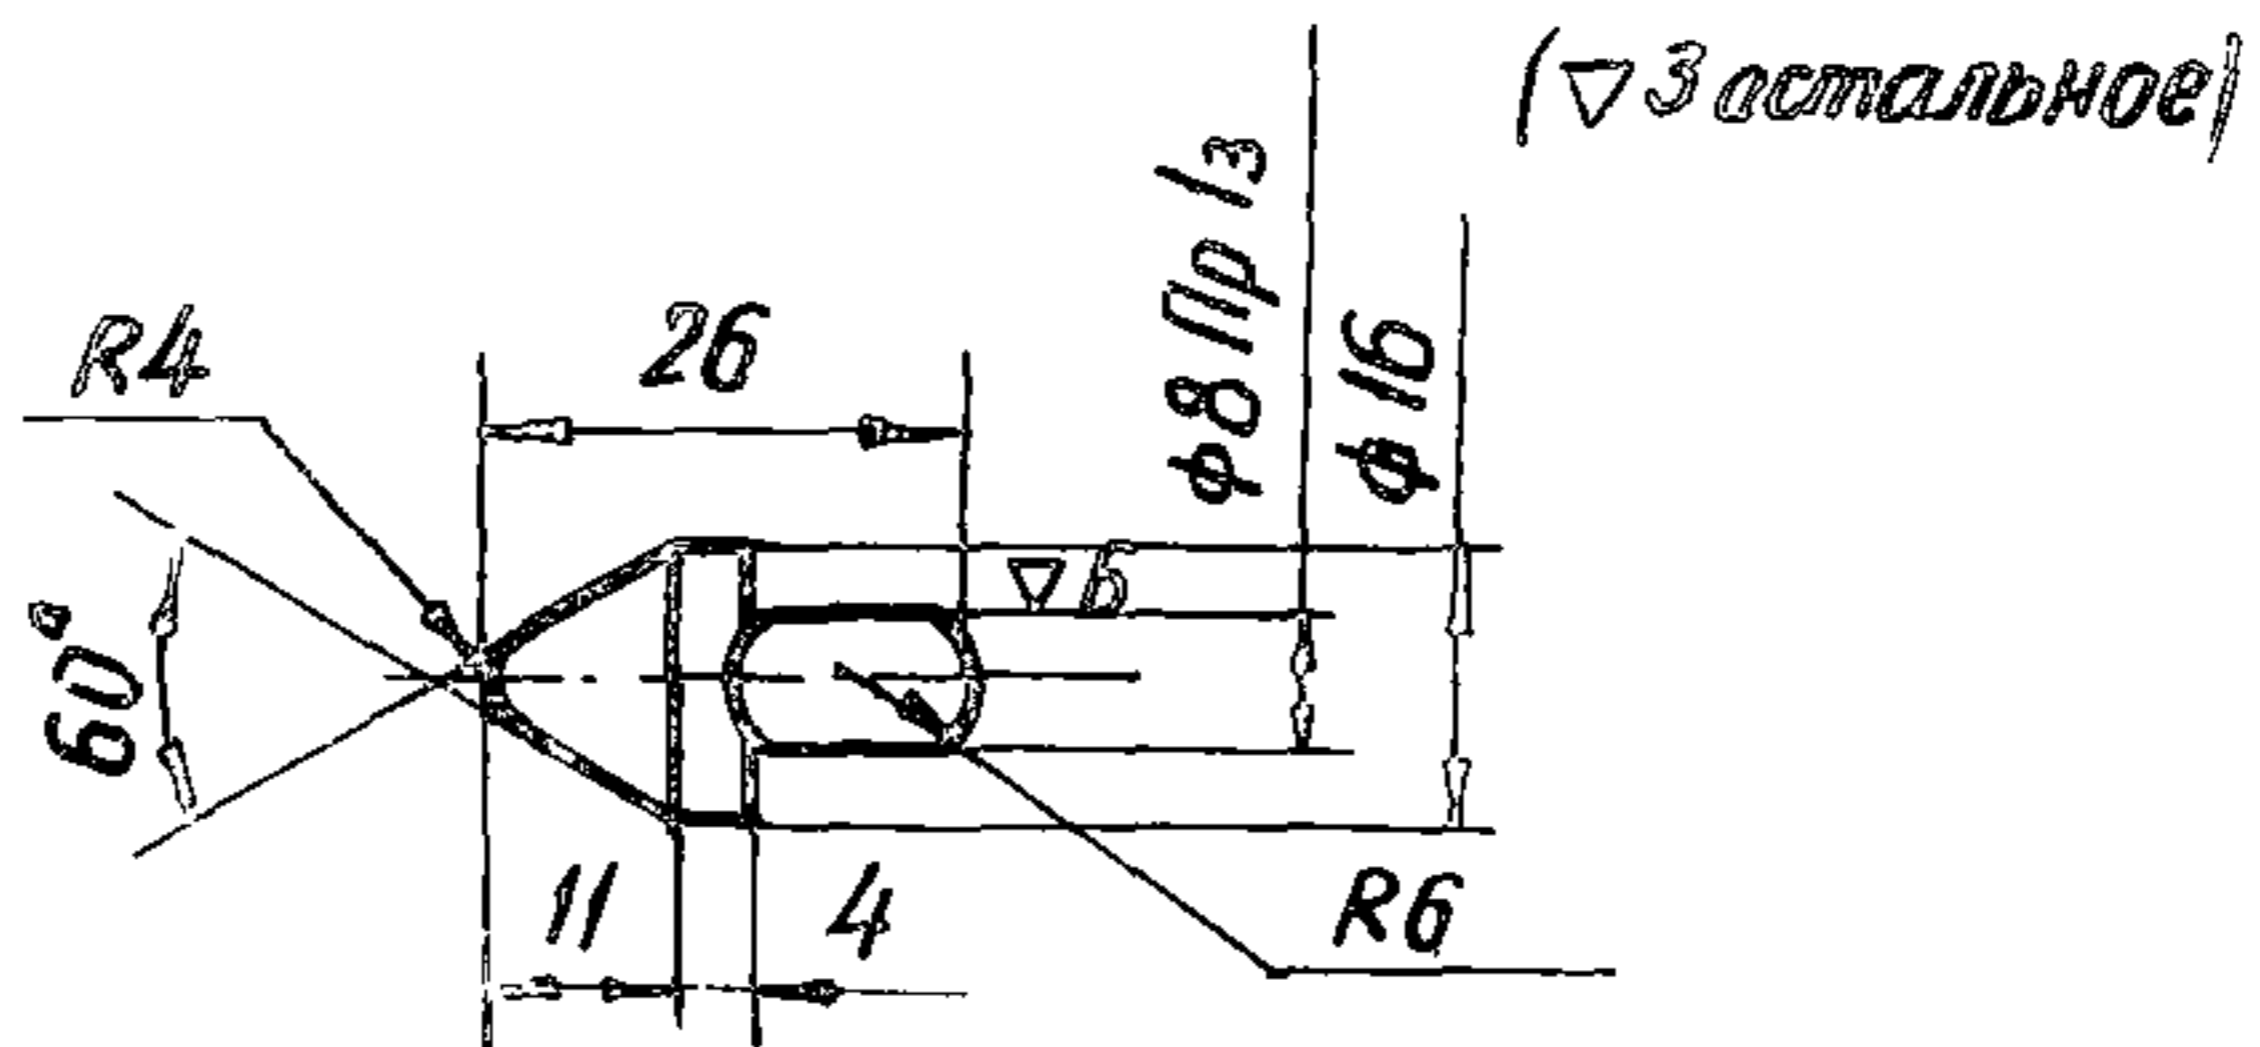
,д. Общий вид прибора. Опора неподвижная (5)
